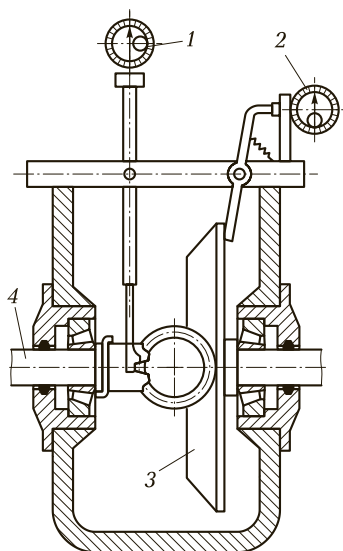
Установка индикаторов контроля сборки конических зубчатых передач:
